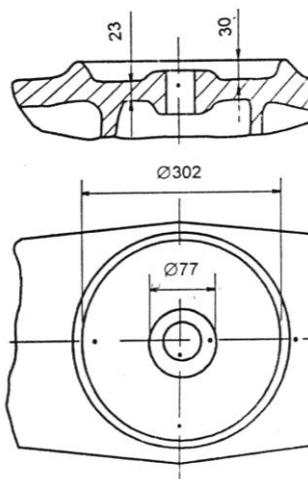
Наплавляемая кольцевая поверхность надрессорной балки
